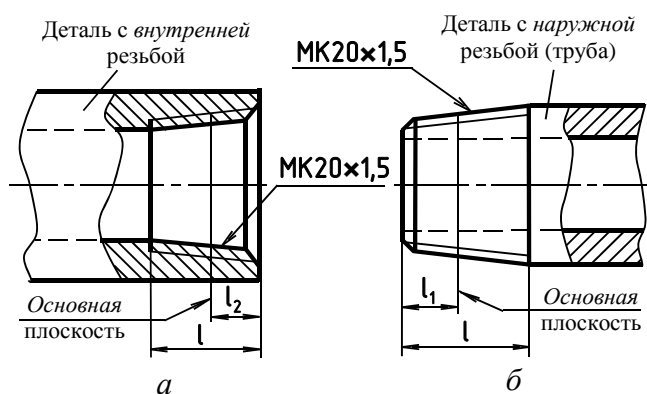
Обозначение на чертеже метрической конической резьбы: а – внутренней; б – наружной
